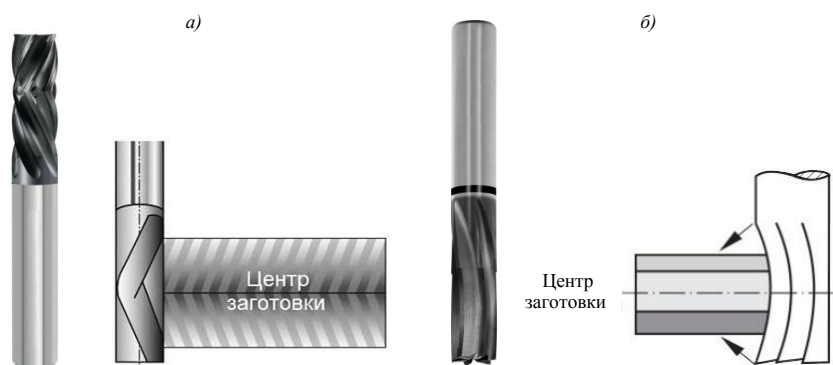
Фрезы для обработки по контуру полимерного композиционного материала: а – с противоположными режущими частями; б – со спиральными стружечными канавками и изогнутыми режущими кромками
